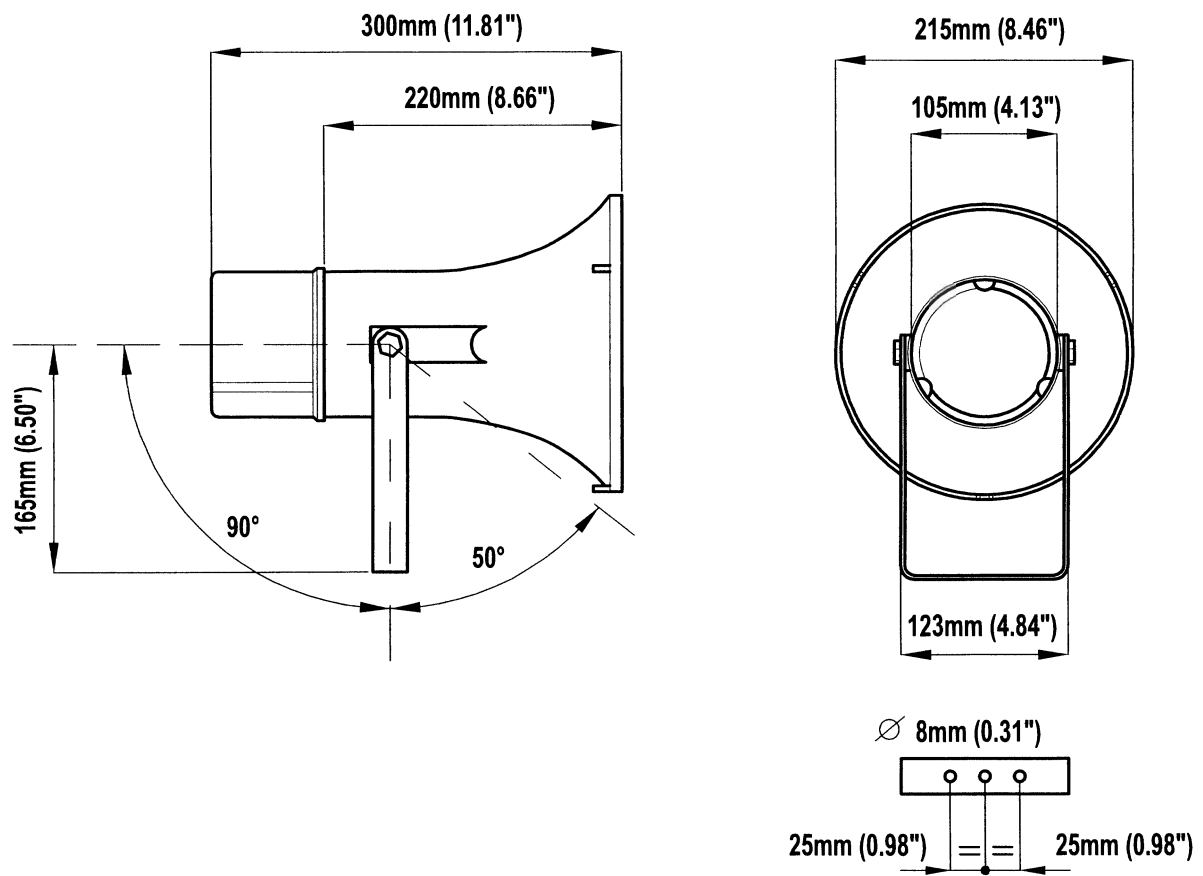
Dimensioni • Dimensions • Dimensions • Abmessungen • Dimensiones
